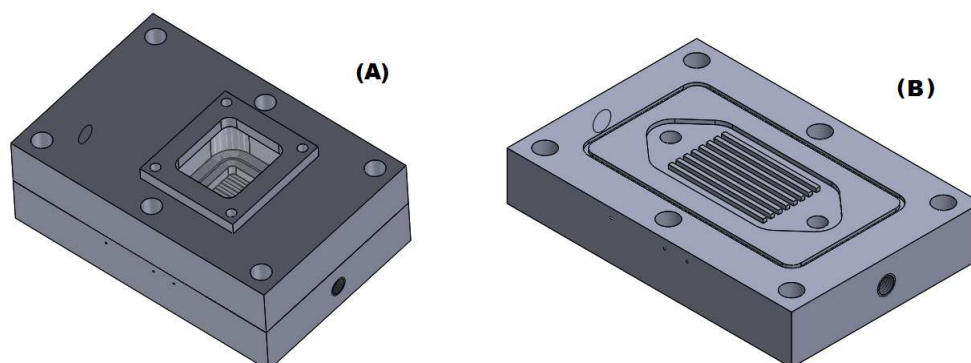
Modelagem da seção de teste 2: (A) Montagem completa (B) vista dos minicanais paralelos.
